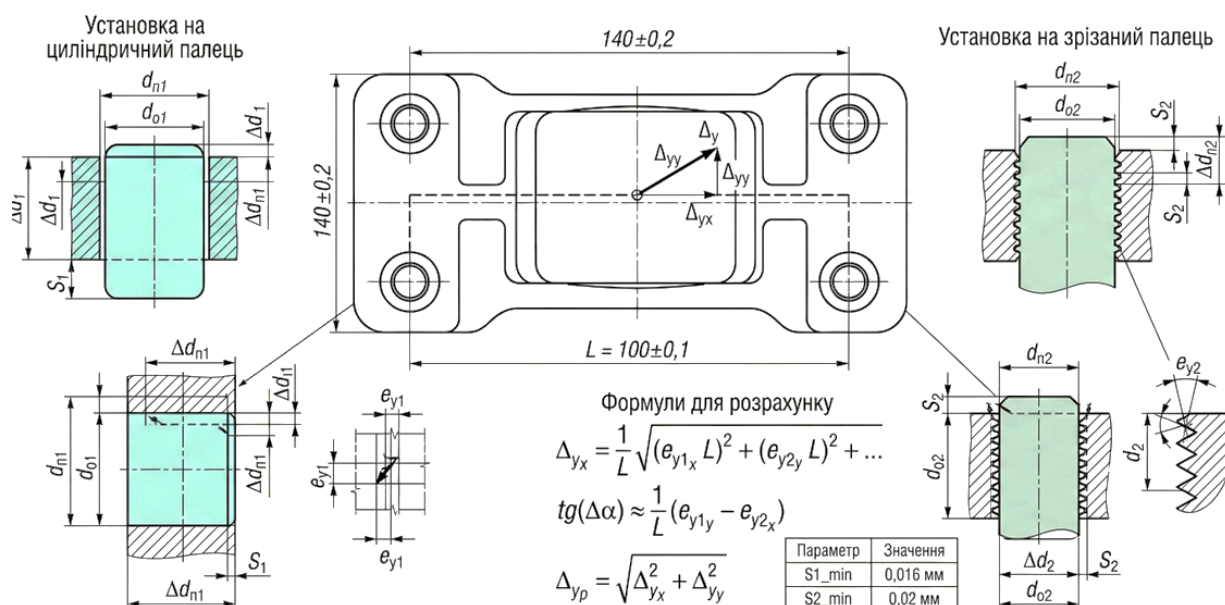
Схема для розрахунку похибки встановлення заготовки на циліндричний та зрізаний палець
